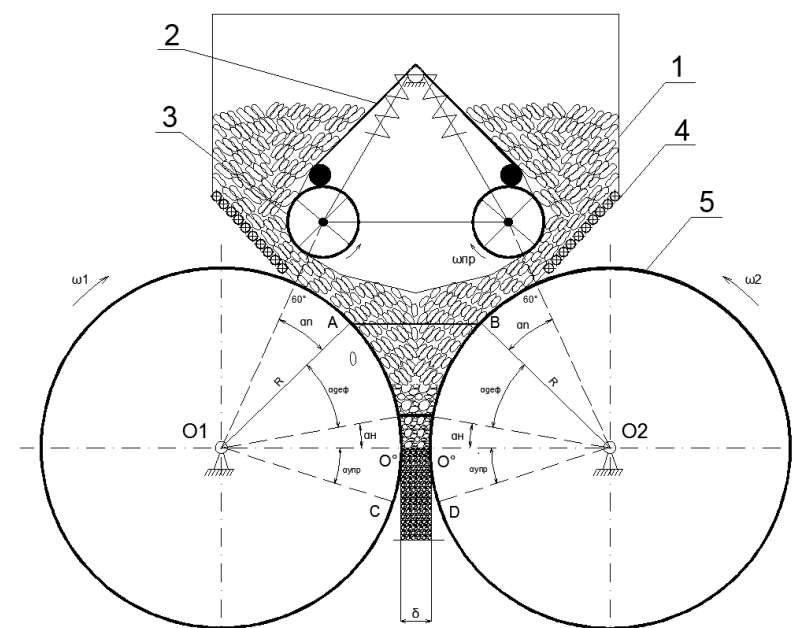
Схема пресс-валкового измельчителя с зубчатыми валками для измельчения сланцевых материалов: 1 – устройство для направленной подачи материала; 2 – подвижные щеки; 3, 4 – направляющие валики; 5 – зубчатые валки
